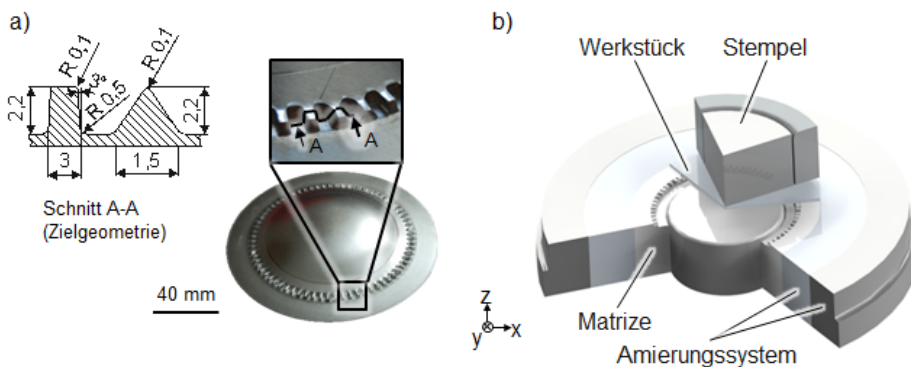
a) Bauteil Fließpressprozess und b) Werkzeugaufbau nach [158]
